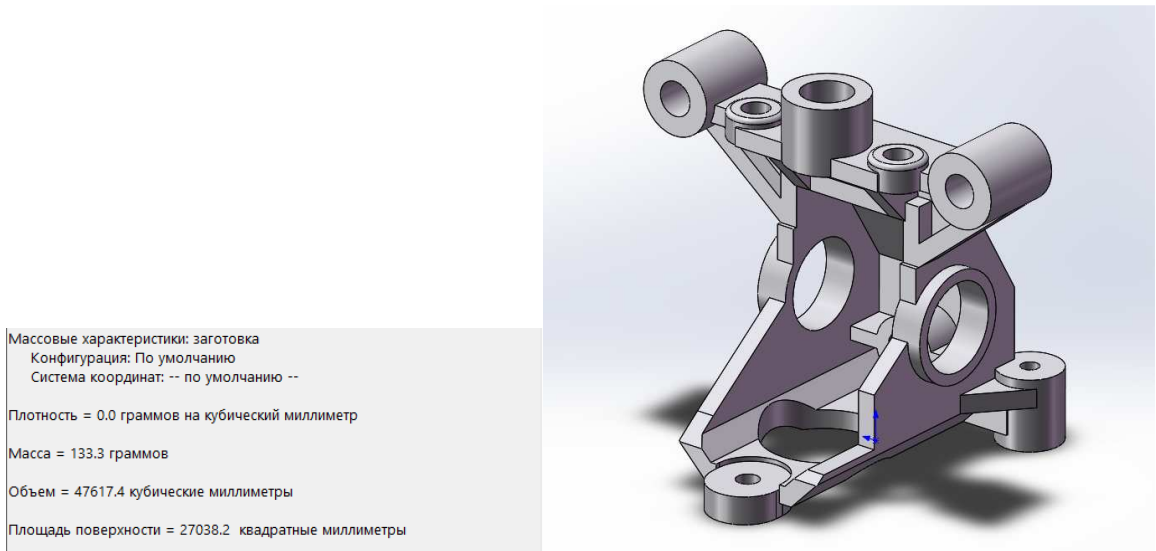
Загальний вигляд 3D-моделі заготовки
